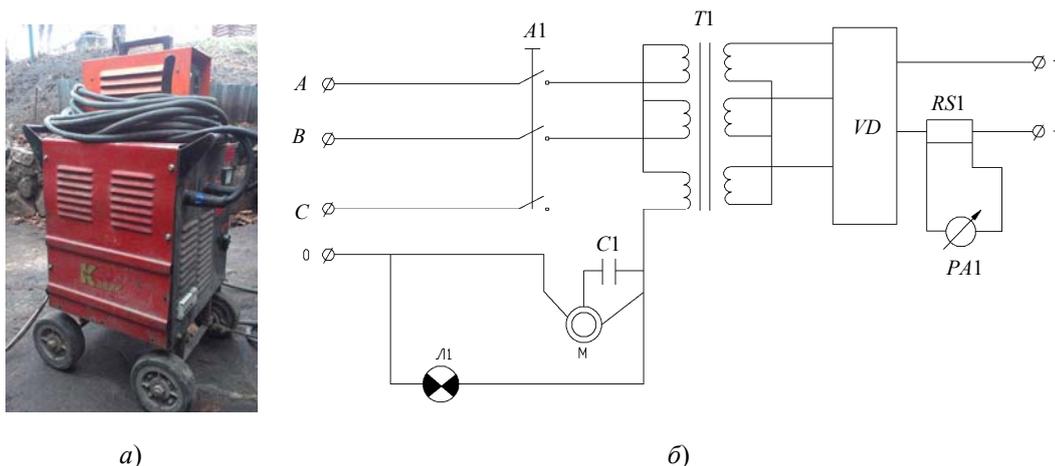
Сварочный трансформатор ВД-301У3:
